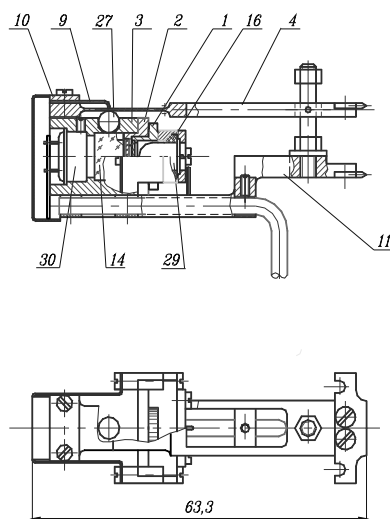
Конструкция датчика для измерения перемещений: 1 — поляризатор, 2 — фазовая пластина, 3 — корпус, 4 — подвижный рычаг, 9 — пружина, 10 — планка, 11 — неподвижный рычаг, 14 — фотоупругий элемент, 27 — шарик, 29 — светодиод, 30 — фотодиод
